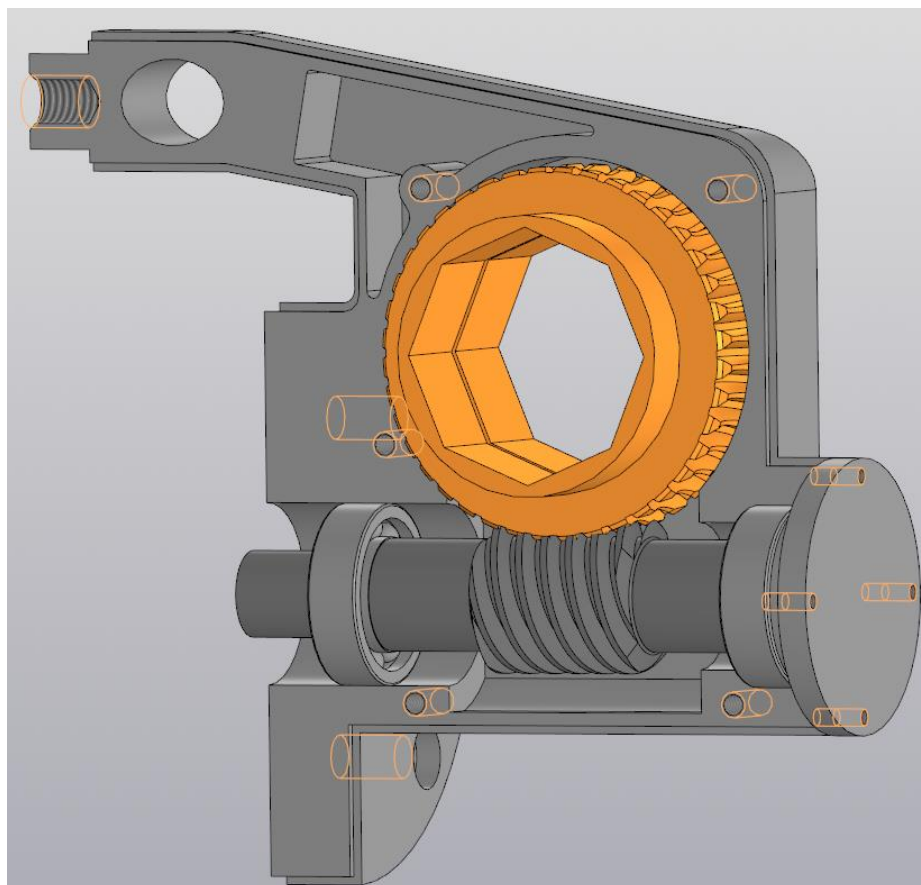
Сборка корпуса с червячной передачей и подшипниками
